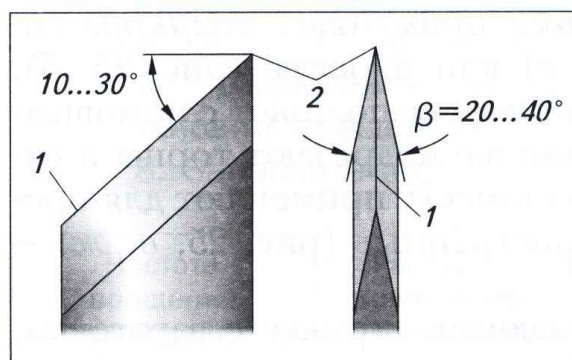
Лезвие косой токарной стамески: 1 – режущая кромка; 2 – вершина
